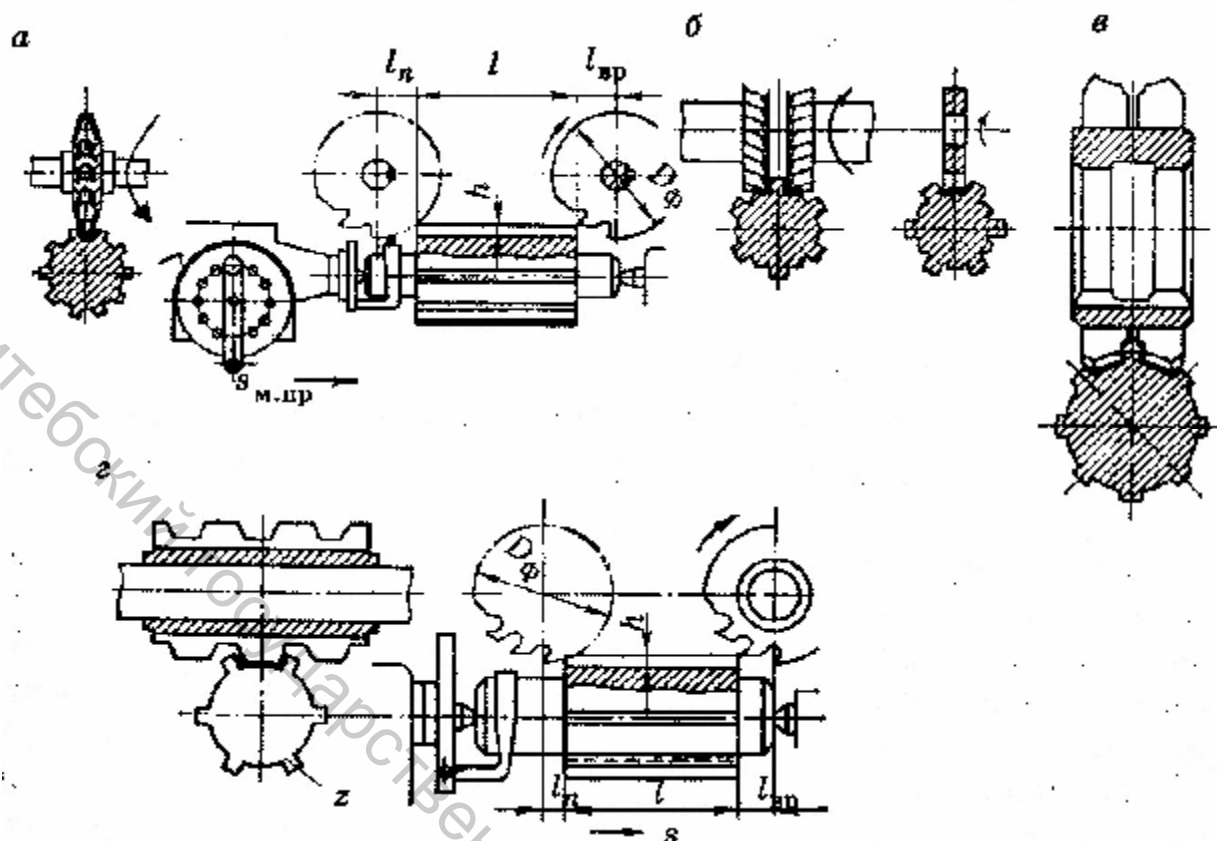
Способы фрезерования шлицев валов: а— шлицевой дисковой фрезой; б— двумя фрезами; в— двумя дисковыми специальными фрезами; г— шлицевой червячной фрезой
